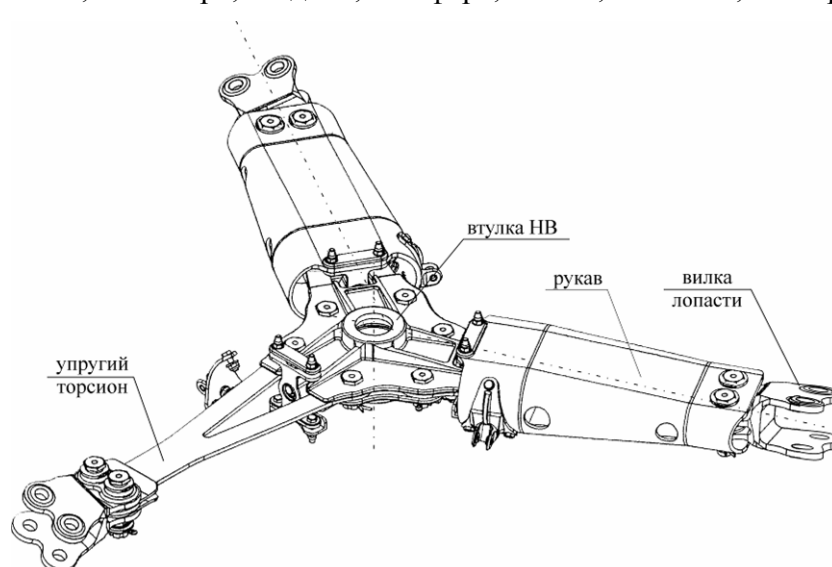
Конструктивная схема втулки несущего винта вертолета
